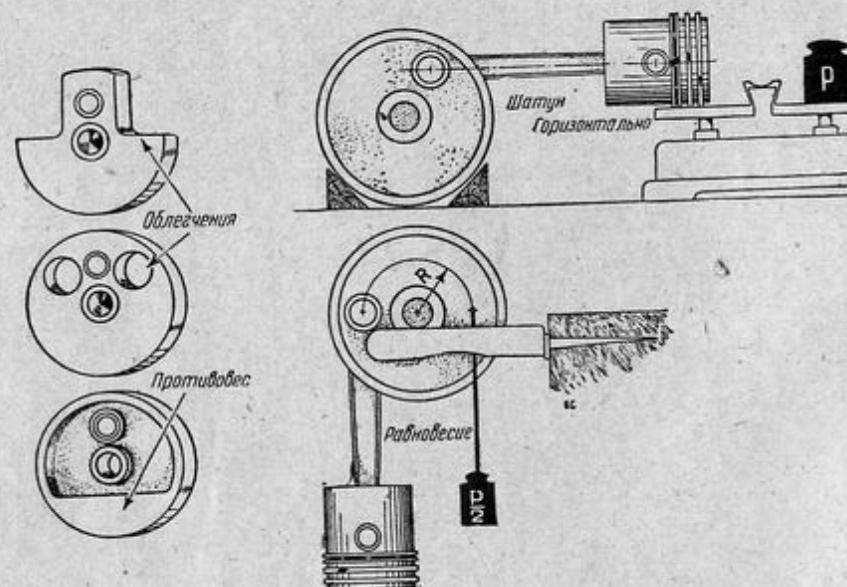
Балансировка коленчатого вала противовесами и их конструкция.
